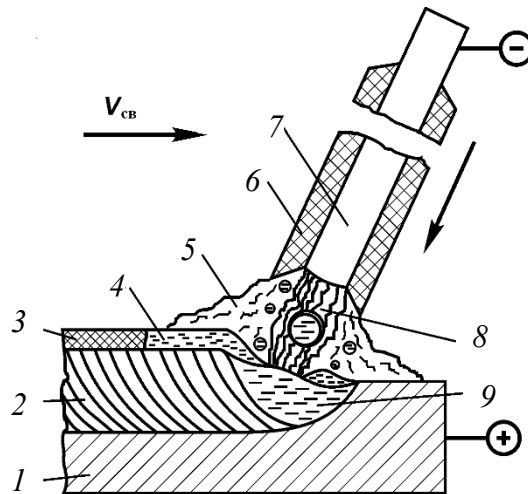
Схема дугового електрозварювання металевим покритим електродом: 1 – зварюваний метал; 2 – зварний шов (наплавлений метал); 3 – тверда шлакова кірка; 4 – рідка шлакова ванна; 5 – газова захисна атмосфера; 6 – покриття електрода; 7 – металевий стрижень зі зварювального дроту; 8 – електрична дуга; 9 – металева ванна; $V_{св}$ – швидкість зварювання
